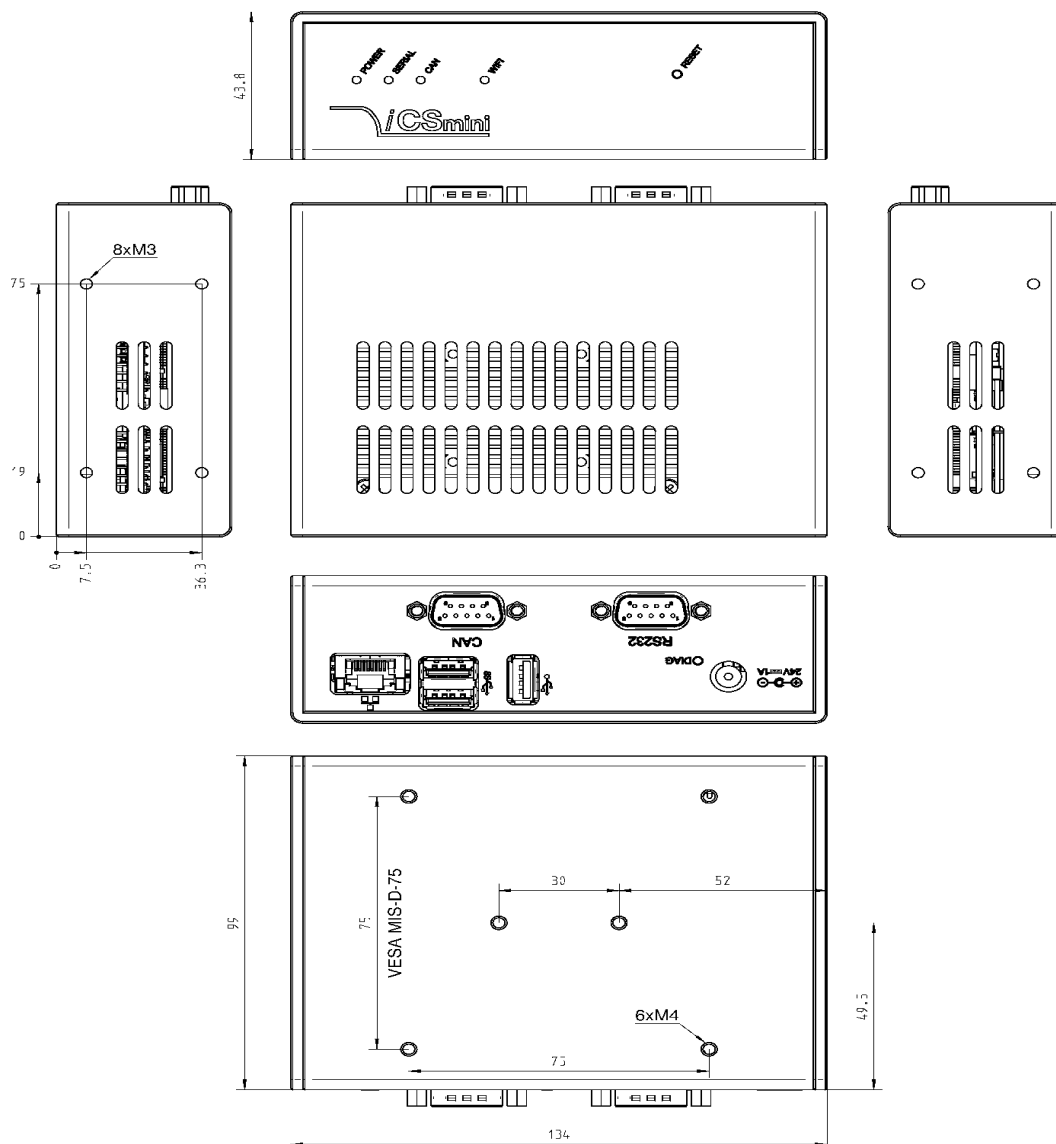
Figure 1: dimensional drawing of iCS2mini
